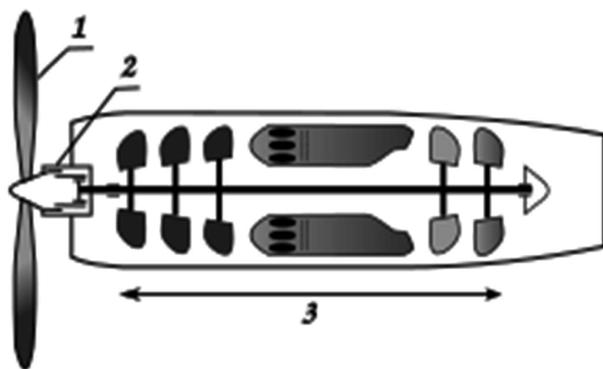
Схема турбовинтового двигателя: 1 –воздушный винт; 2– редуктор;
